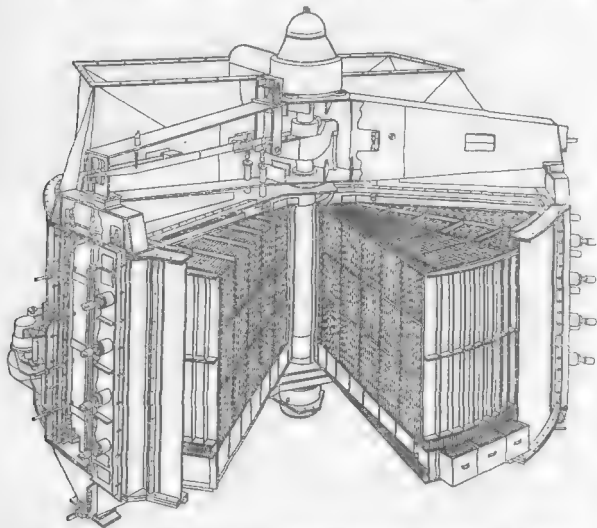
Общий вид РВП КАГ с вертикальной осью вращения и верхним расположением опоры
